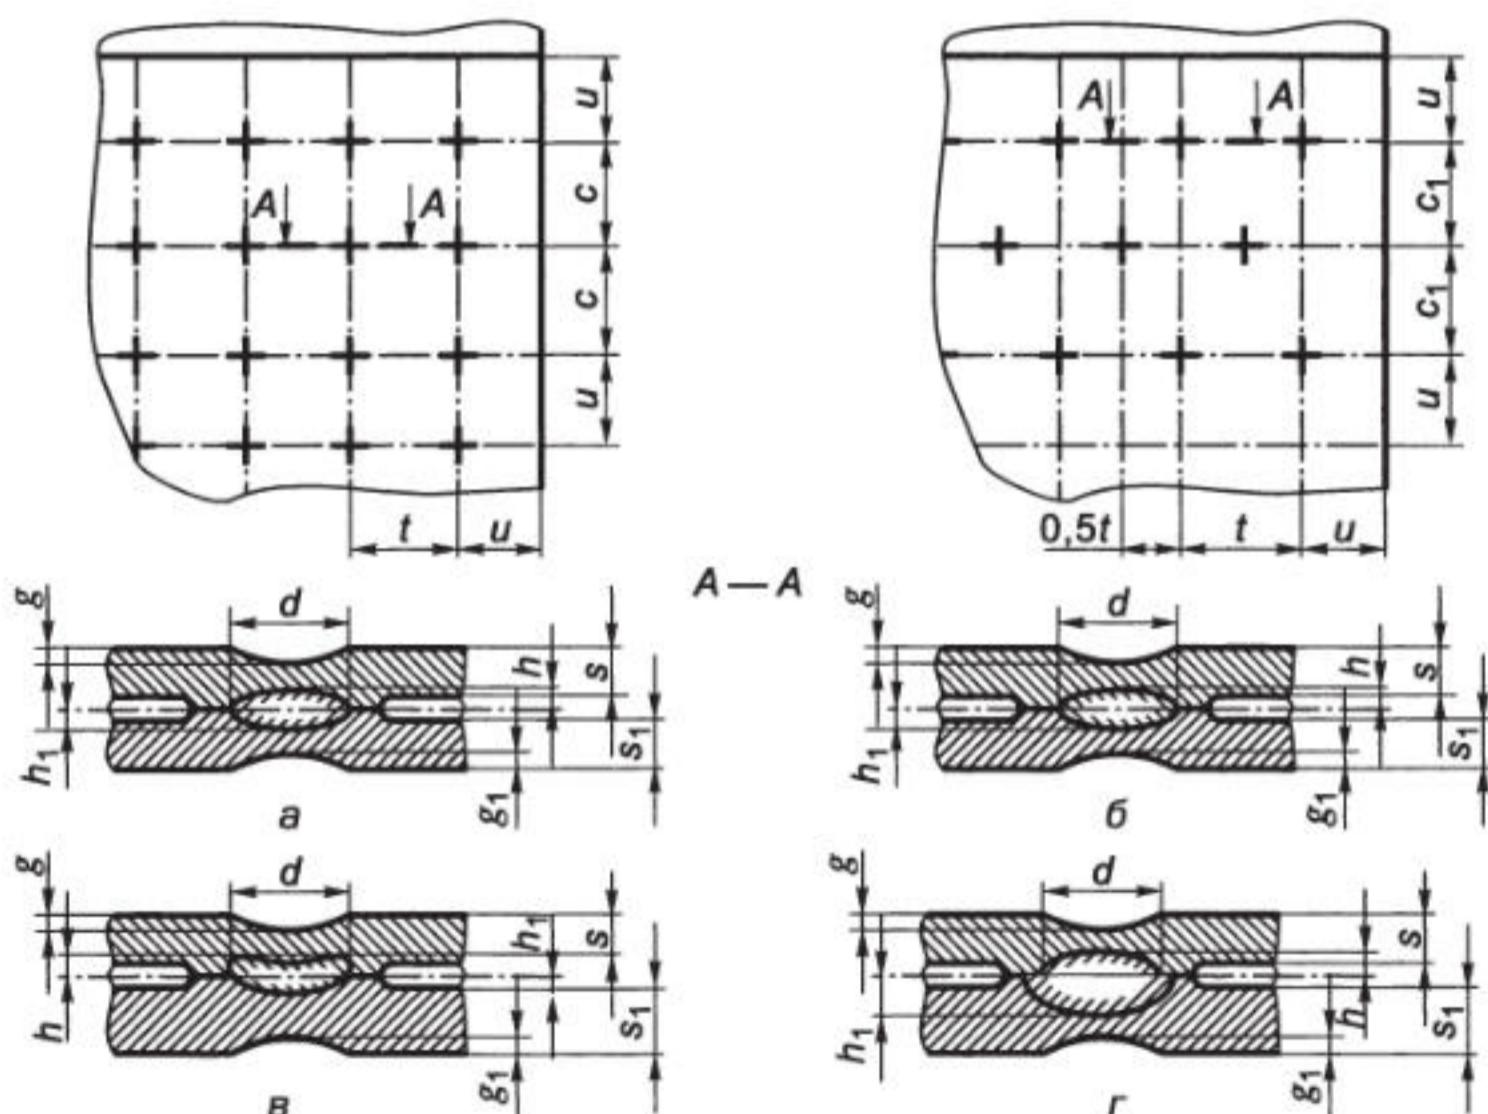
Конструктивные элементы соединений контактной точечной сваркой:
